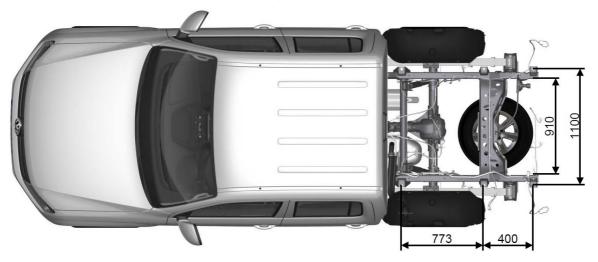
Vista dall'alto dell'Amarok DC senza cassone
